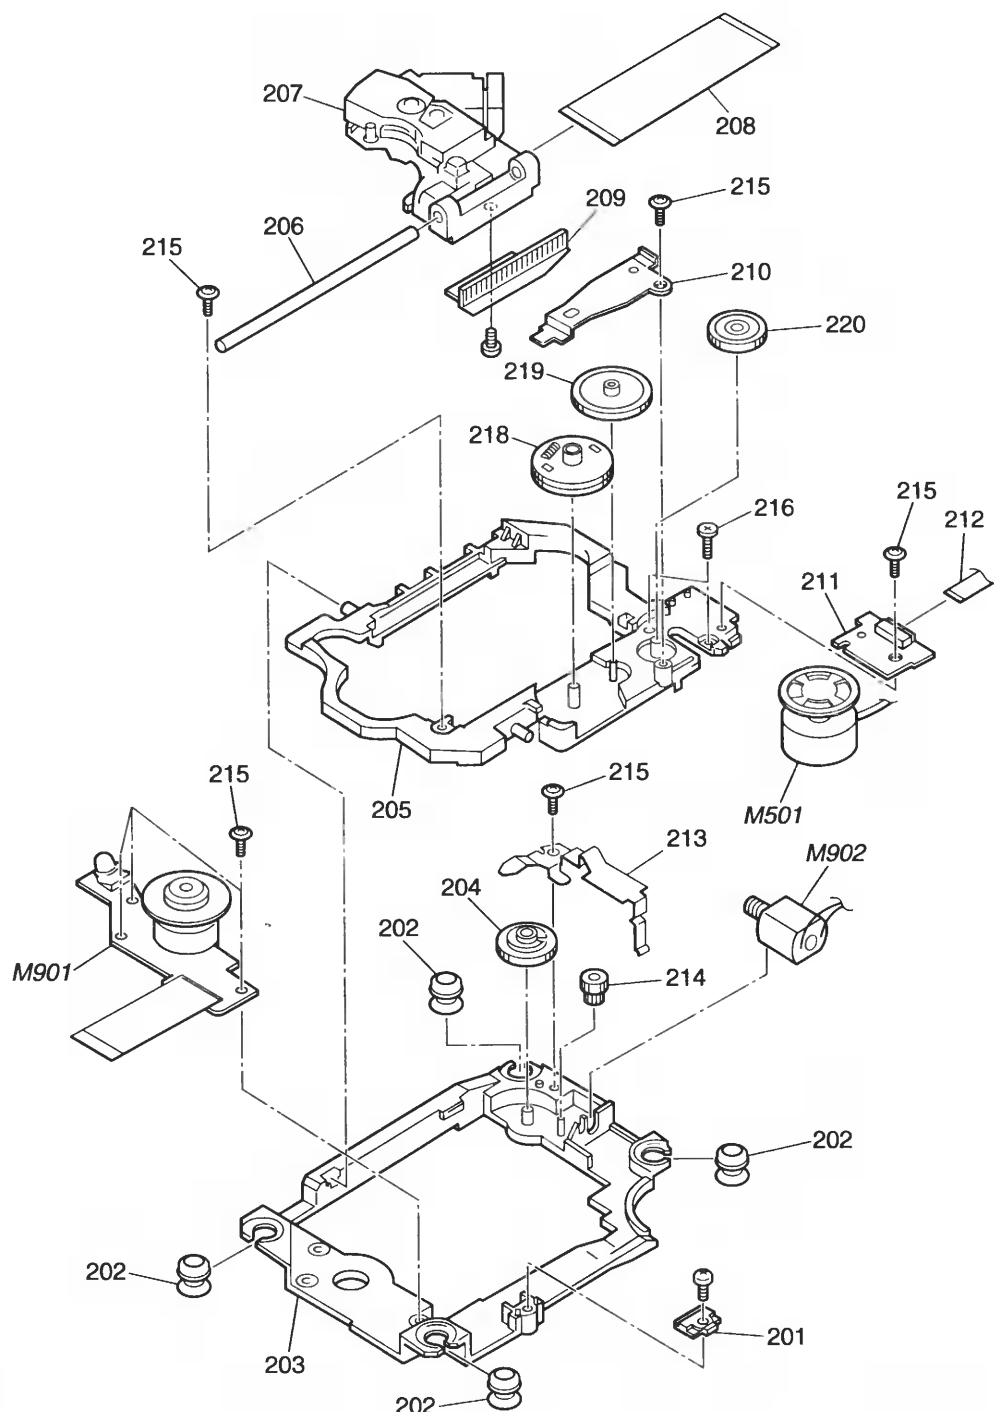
Сборочный чертеж механизма привода дисков условного типа 2
